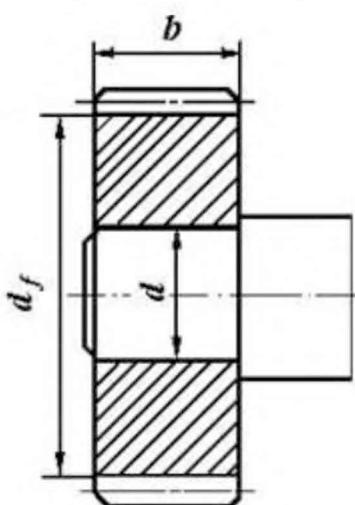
Цилиндрическое соединение вала и шестерни с натягом
